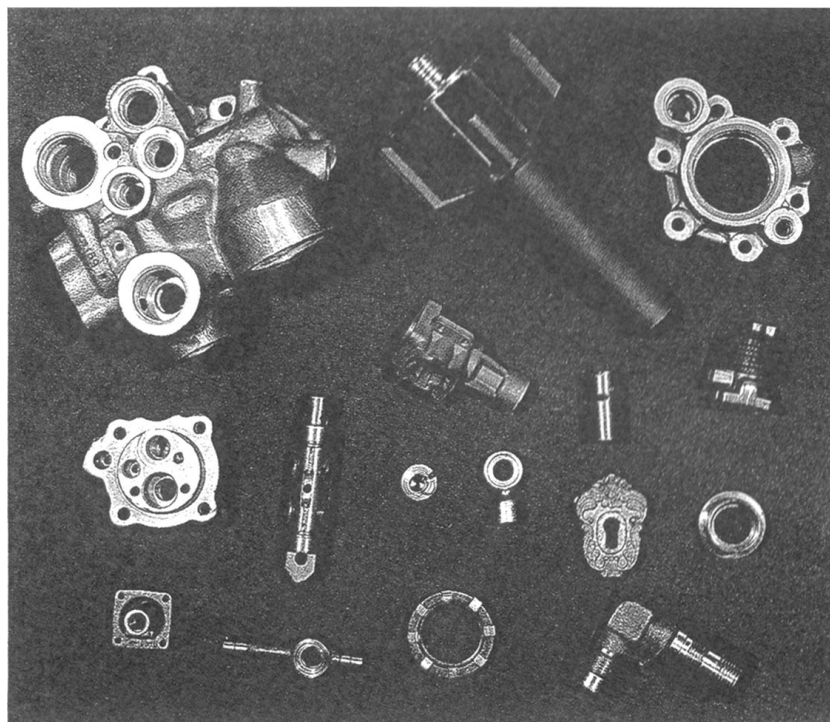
Примеры обрабатываемых деталей на установке Т-15
